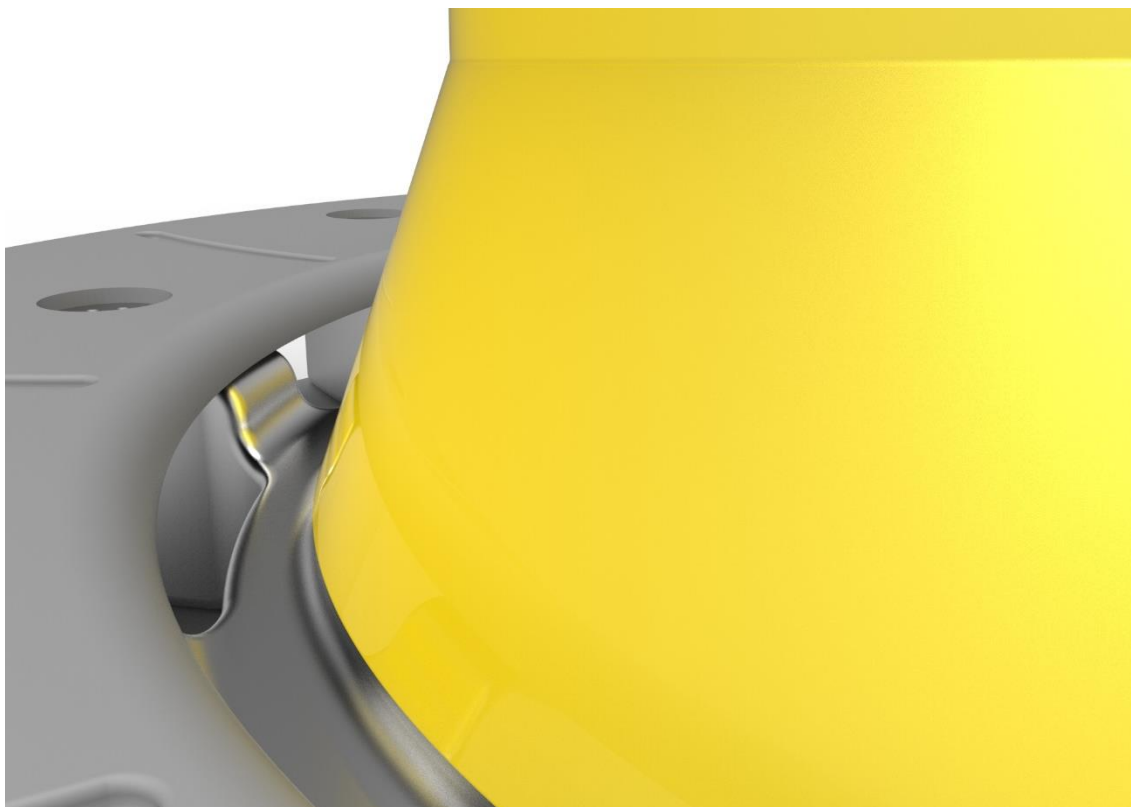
Detalle canal 2, perspectiva interior canal y unión campana
